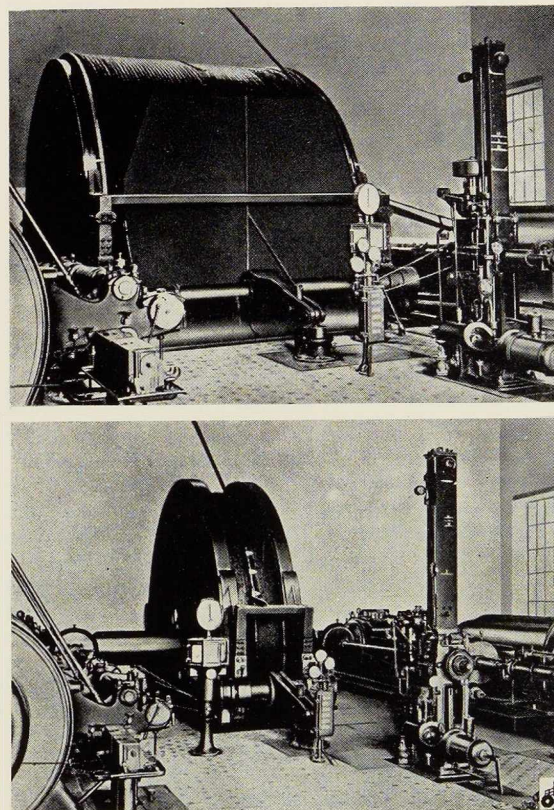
Ensemble d'une machine à vapeur installée en 1902 (en haut) équipée vers 1945 d'une poulie Koepe soudée (en bas).
